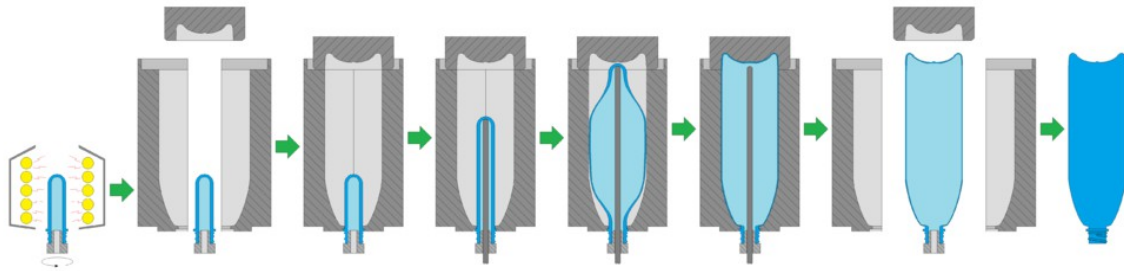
Procédé de moulage par soufflage [Ricardo Weyh]
